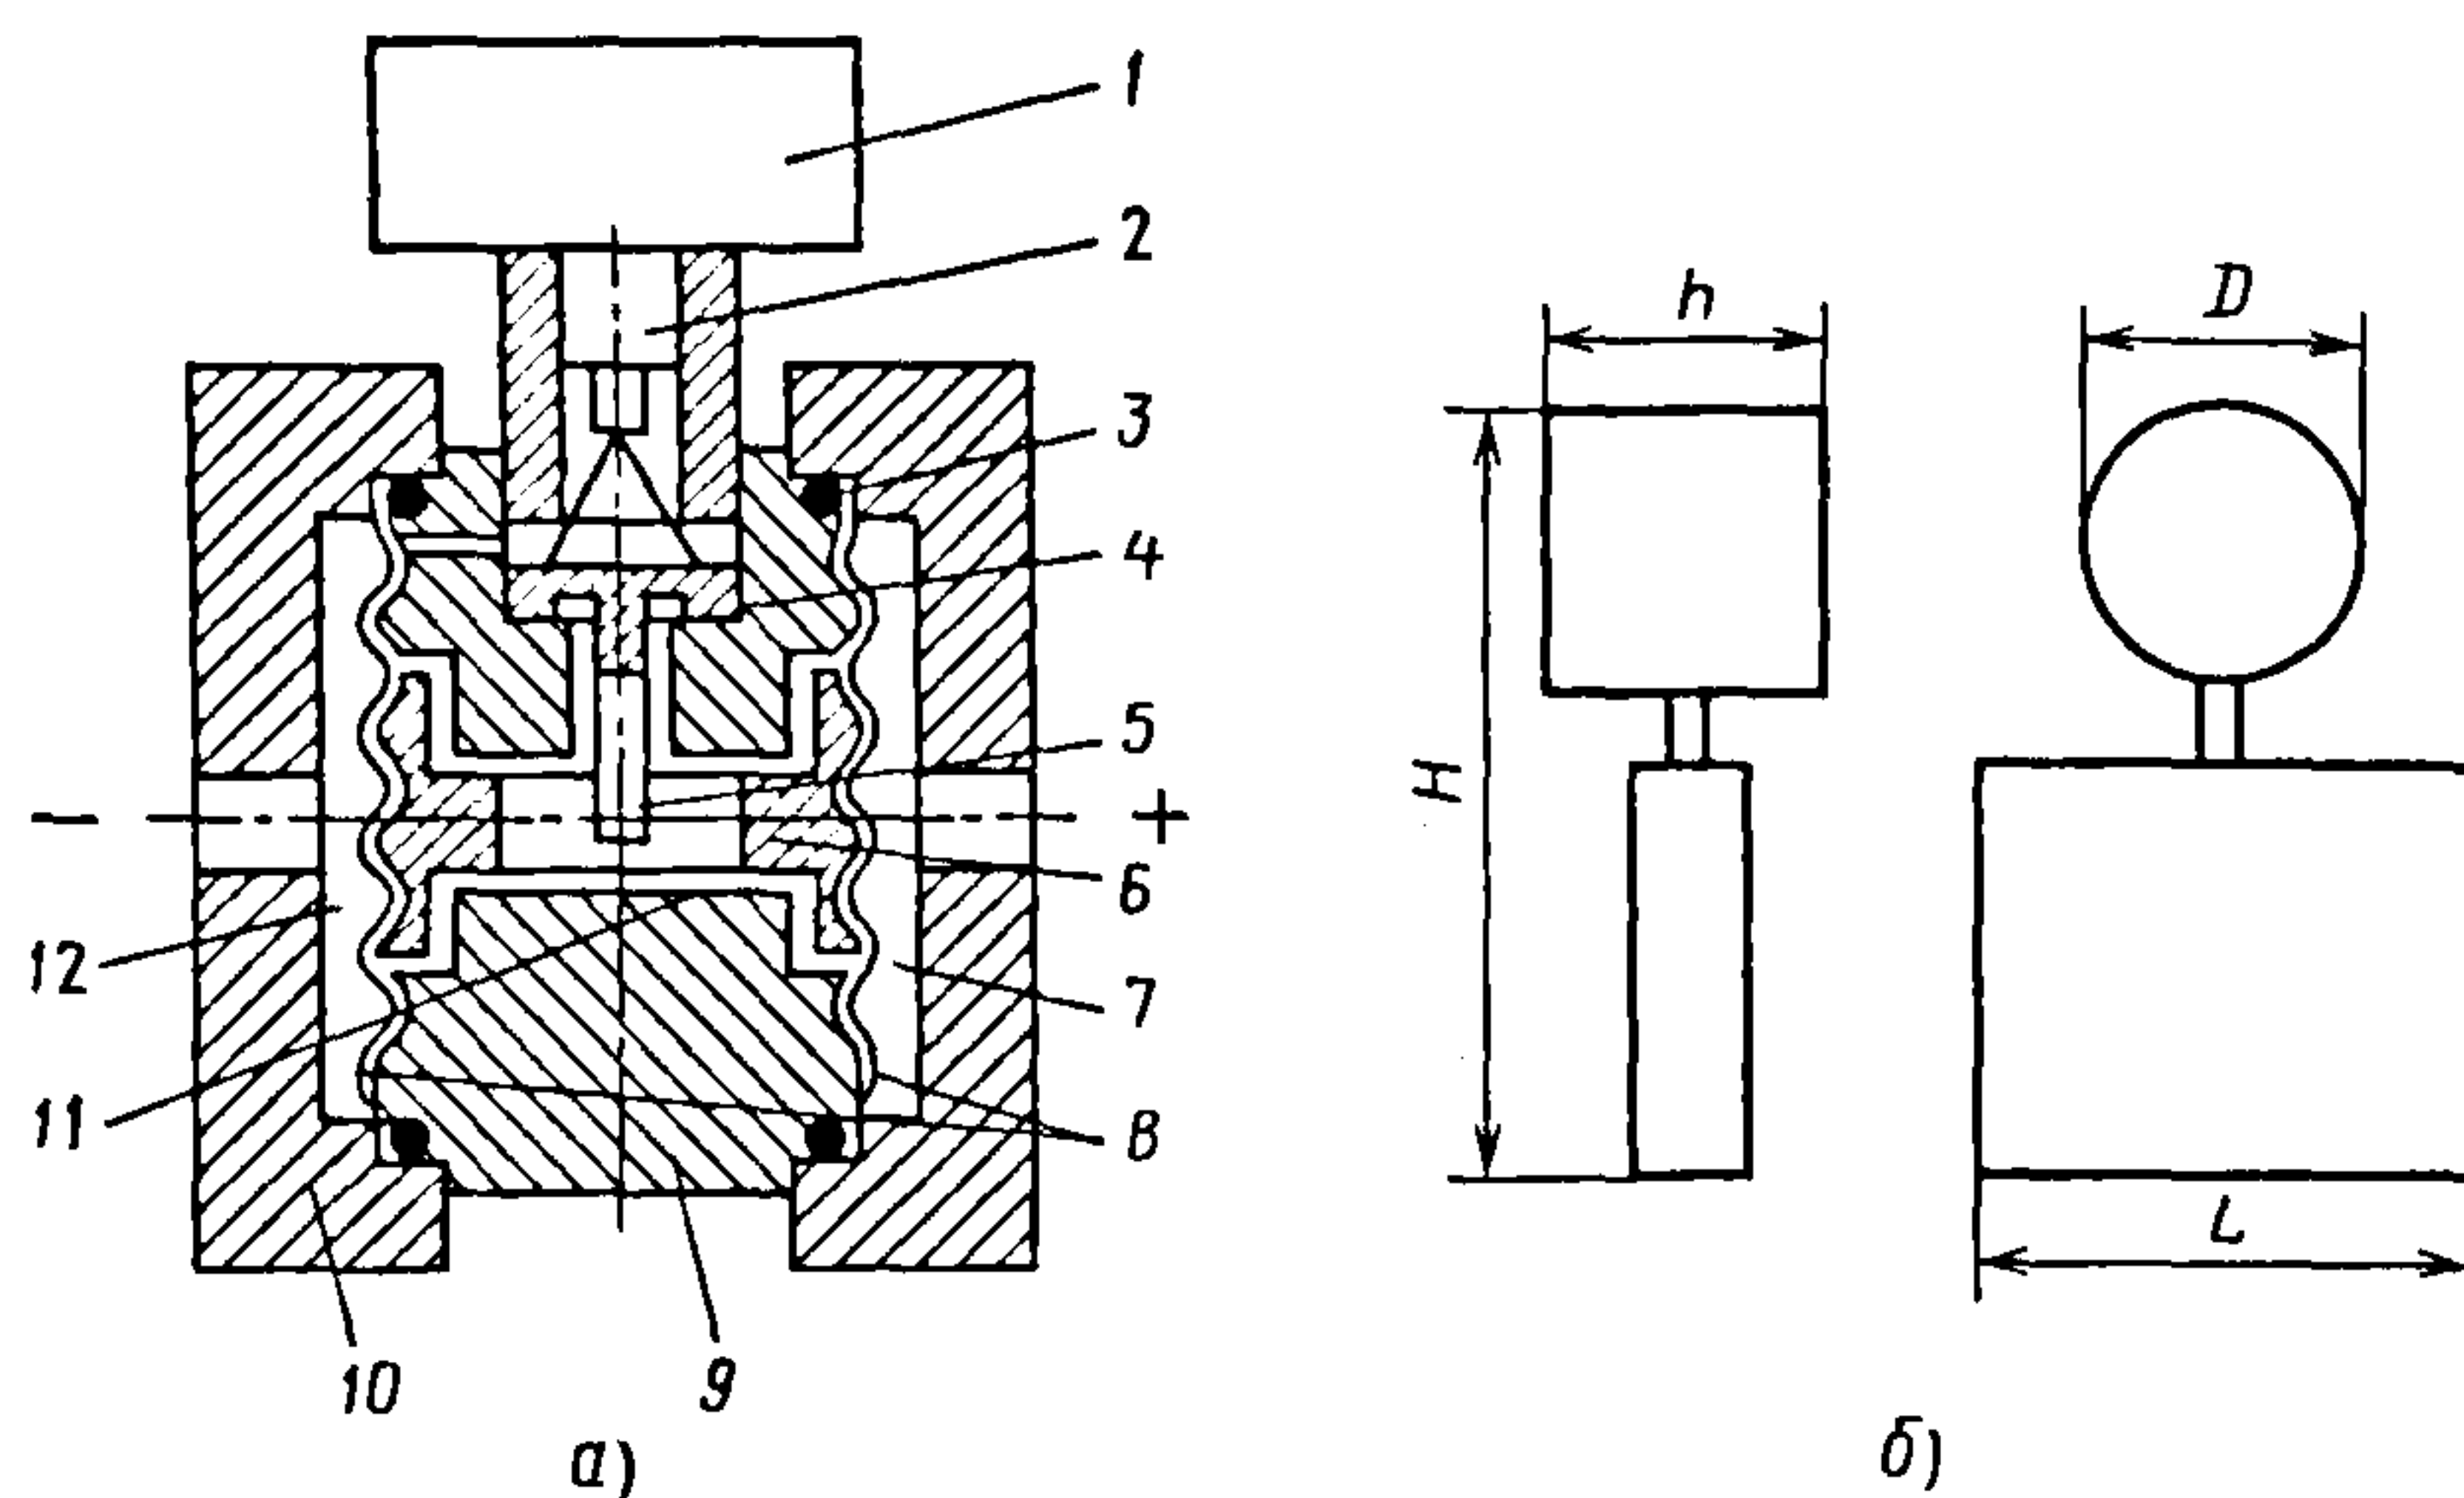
Схема (а) и габаритный чертеж (б) преобразователя «Сапфир-22»
